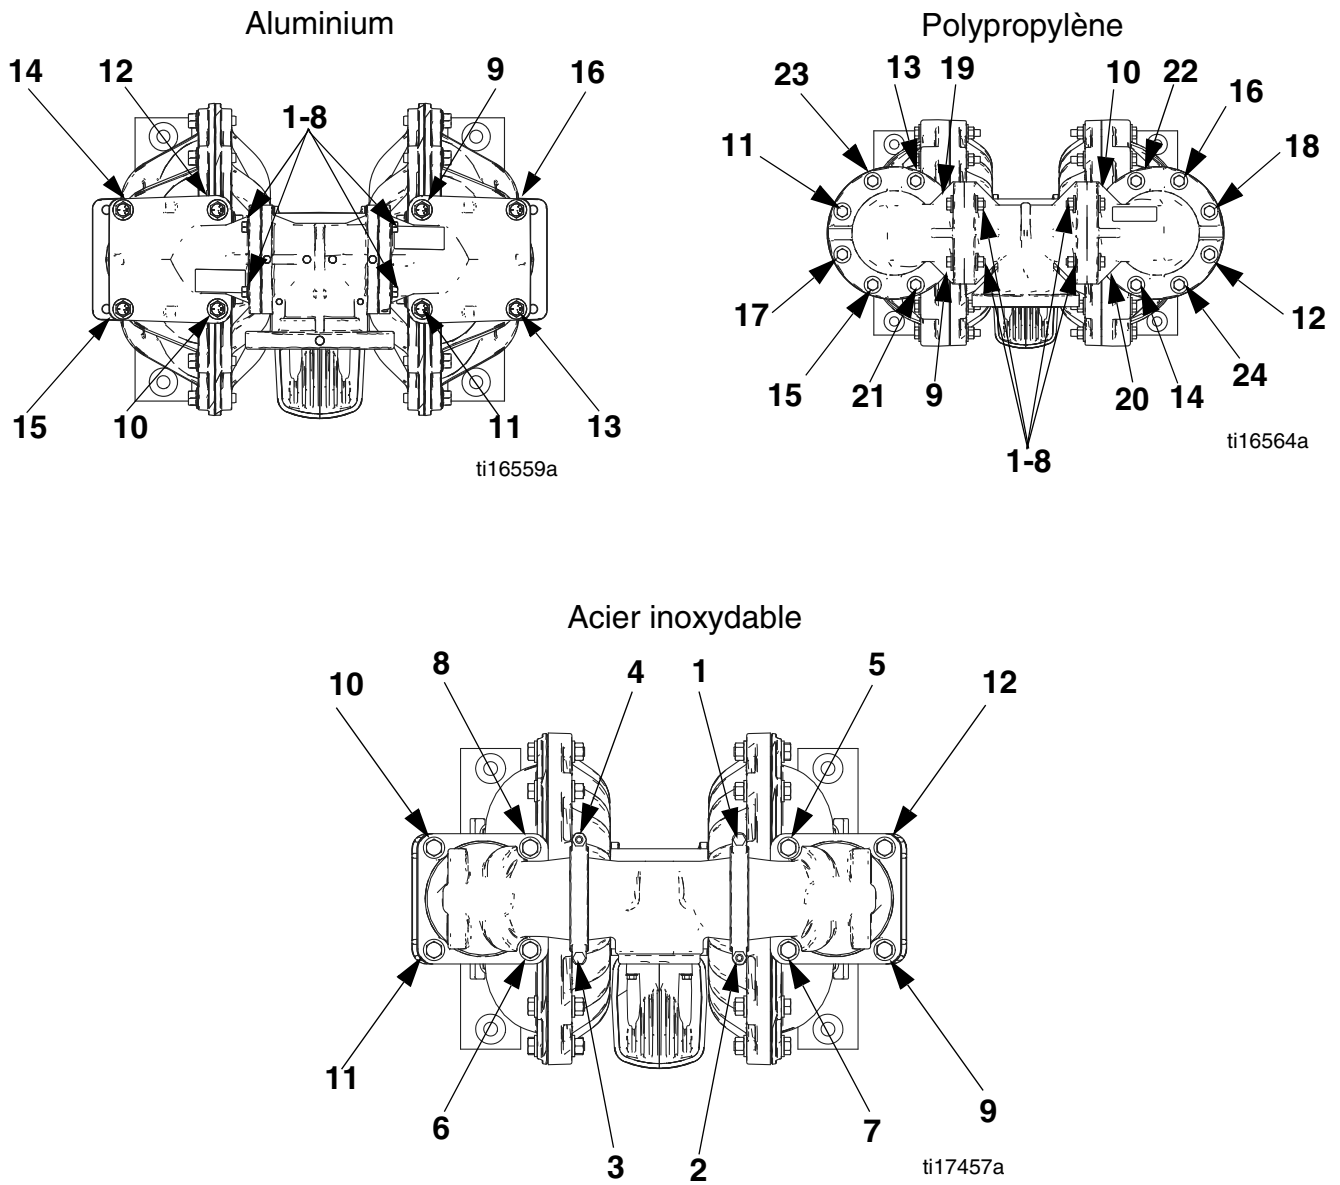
Instructions concernant les couples de serrage - Fixations du collecteur
